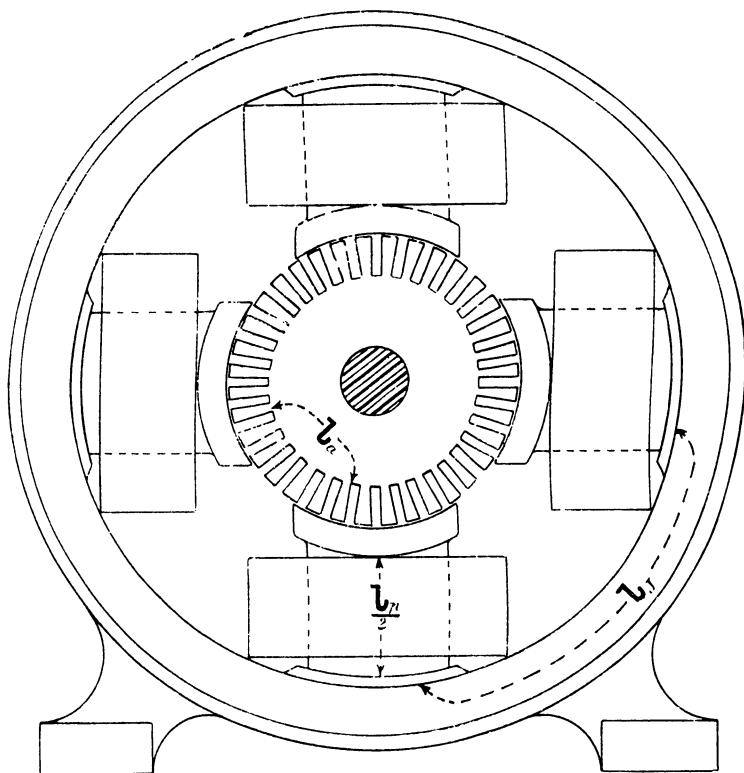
Schnittzeichnung einer vierpoligen Maschine.
